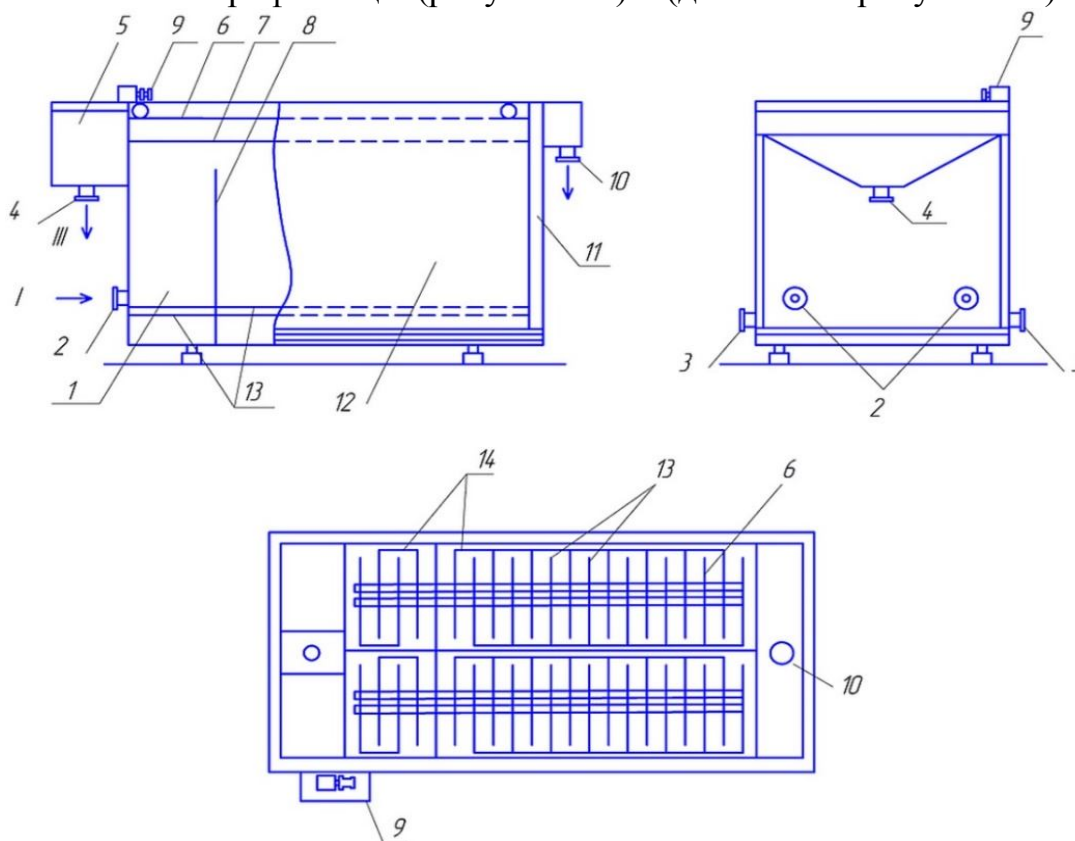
Схема електрофлотатора: 1 - камера флокуляції (грубої очистки); 2 - патрубки для подачі стічної води; 3 - патрубки для дренажу (технологічного зливу); 4 - патрубок для відведення шламу; 5 - камера для збору шламу; 6 - пінозбірний пристрій; 7 - рівень води в апараті; 8 - перегородки; 9 - електродвигун; 10 - патрубок для відведення очищеної води; 11 - гідрозатвор; 12 - камера флотації (тонкої очистки); 13 - електродні блоки; 14 – струмопідведення; потоки: I - стічна вода, II - очищена вода, III - флотошлам
